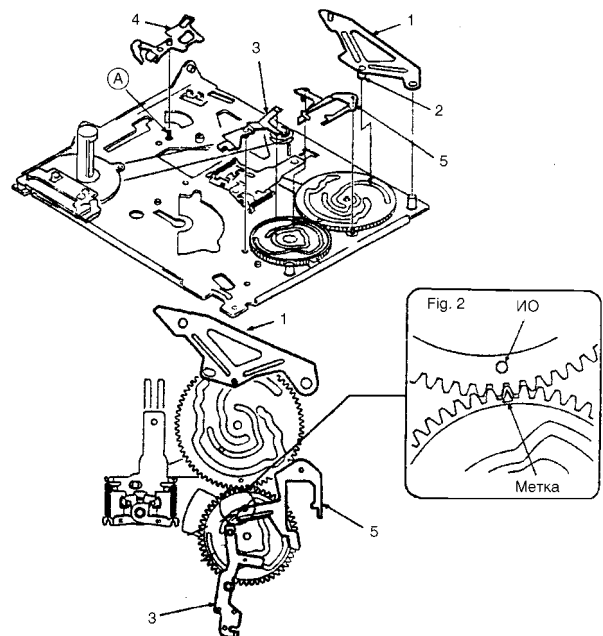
Демонтаж и установка рычага LS, рычага привода HC, пластины прижима и пластины регулятора натяжения
